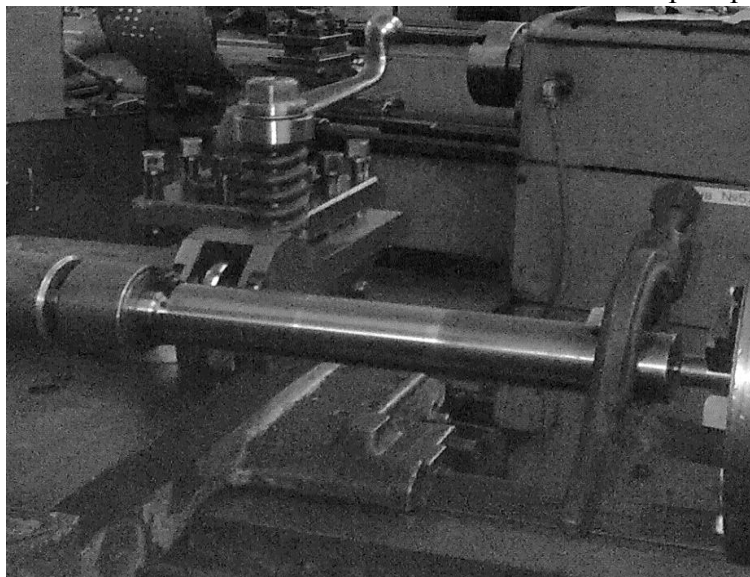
Обкатування вала накатним роликом на верстаті 1К62
